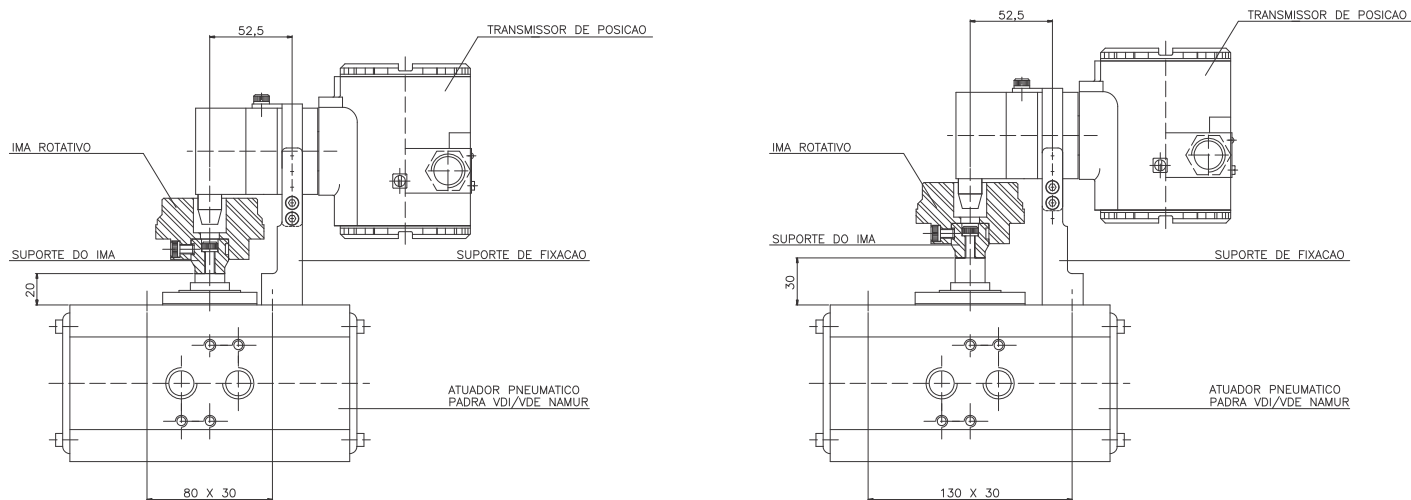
b – Desenho Dimensional do Sensor Remoto
